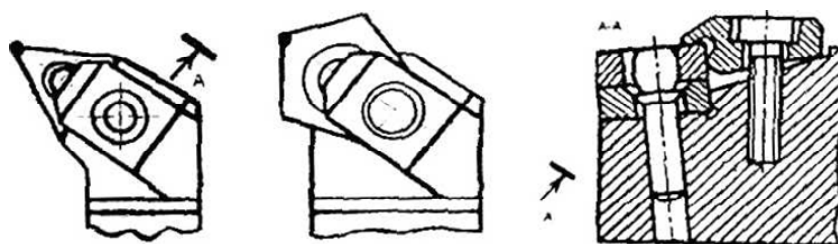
Эскизы рабочей части сборных инструментов: тип крепления РВ
